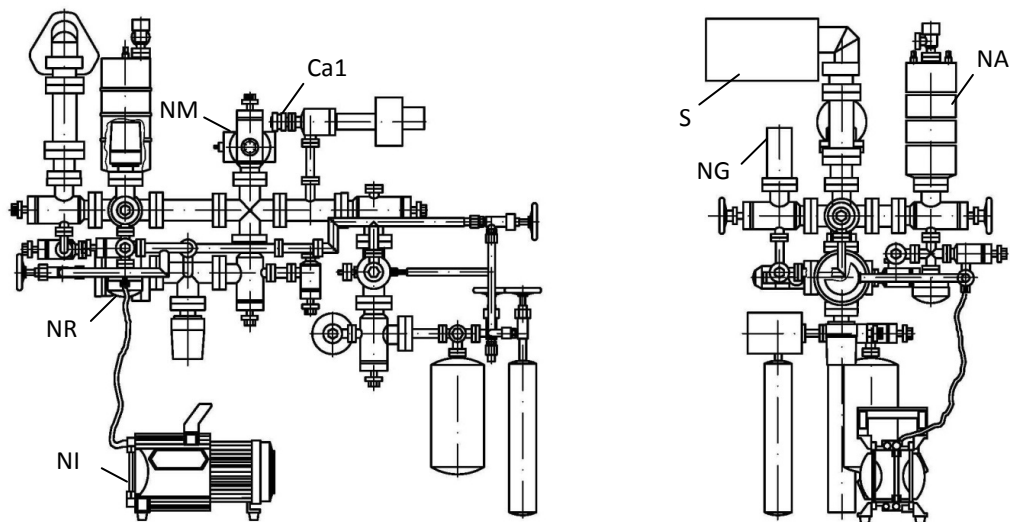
Компоновочный чертеж модернизированной установки финишного контроля герметичности разрядников.
